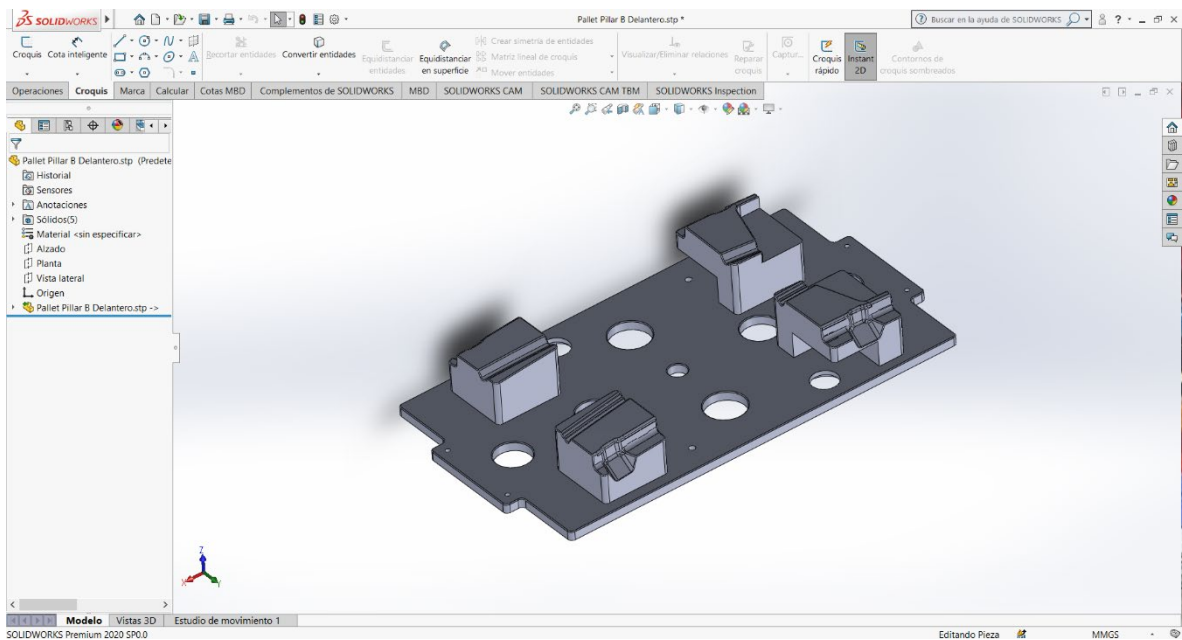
Base de soporte de molduras con detalle en pallets A y B
